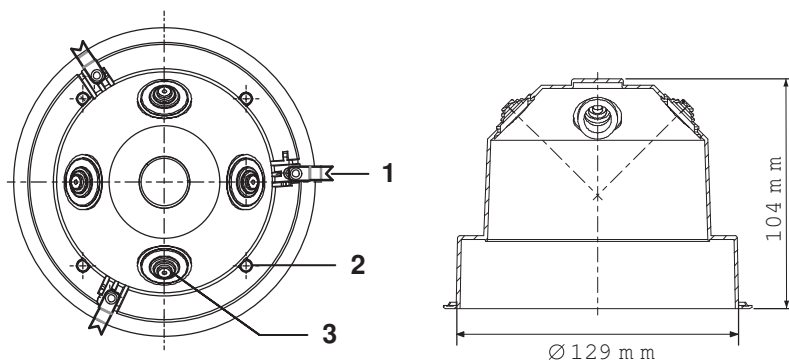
Вид сверху и сбоку корпуса для монтажа в потолок FAA-500-BB
